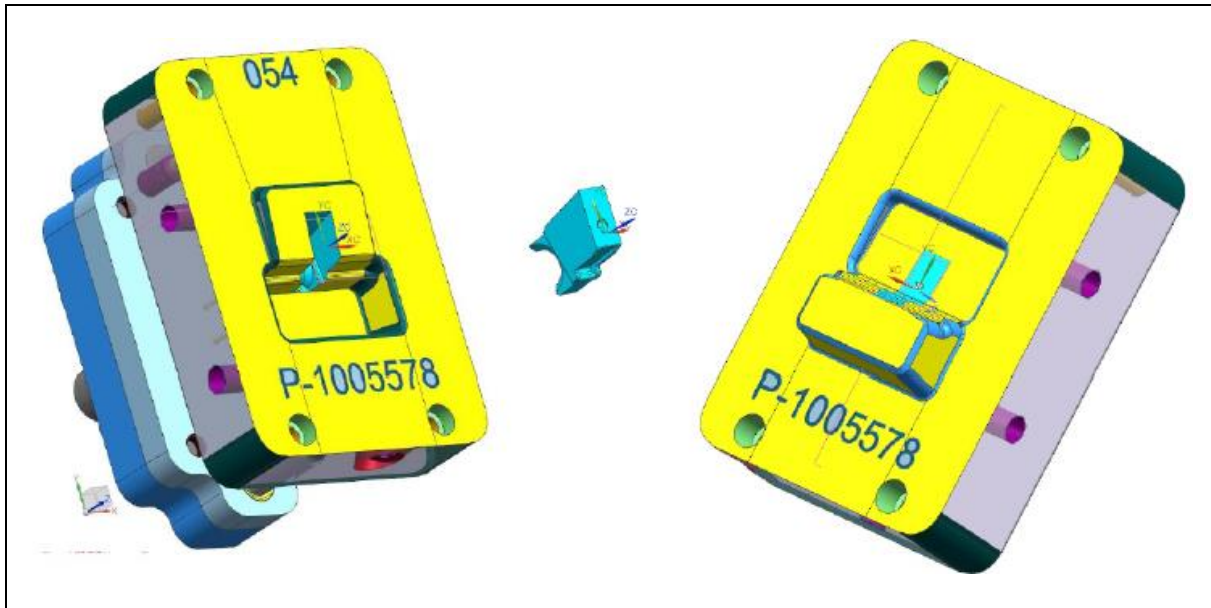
CAD-Modell für zweites Spritzgusswerkzeug (P1005578) und Spritzling mit optimierter Geometrie
